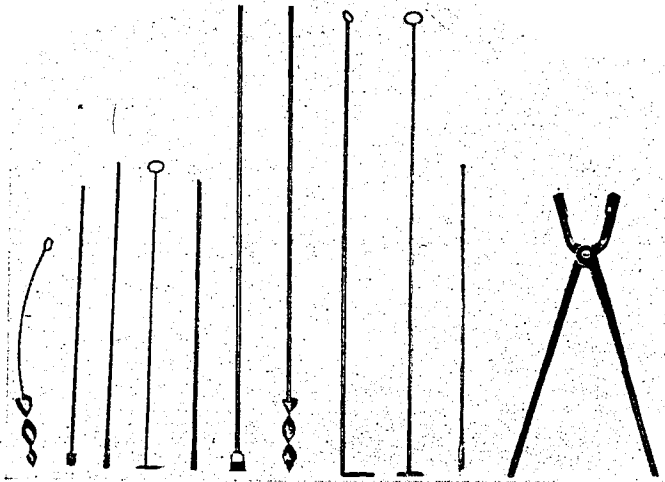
Werkzeuge zum Bedienen der Retorten-Öfen.
